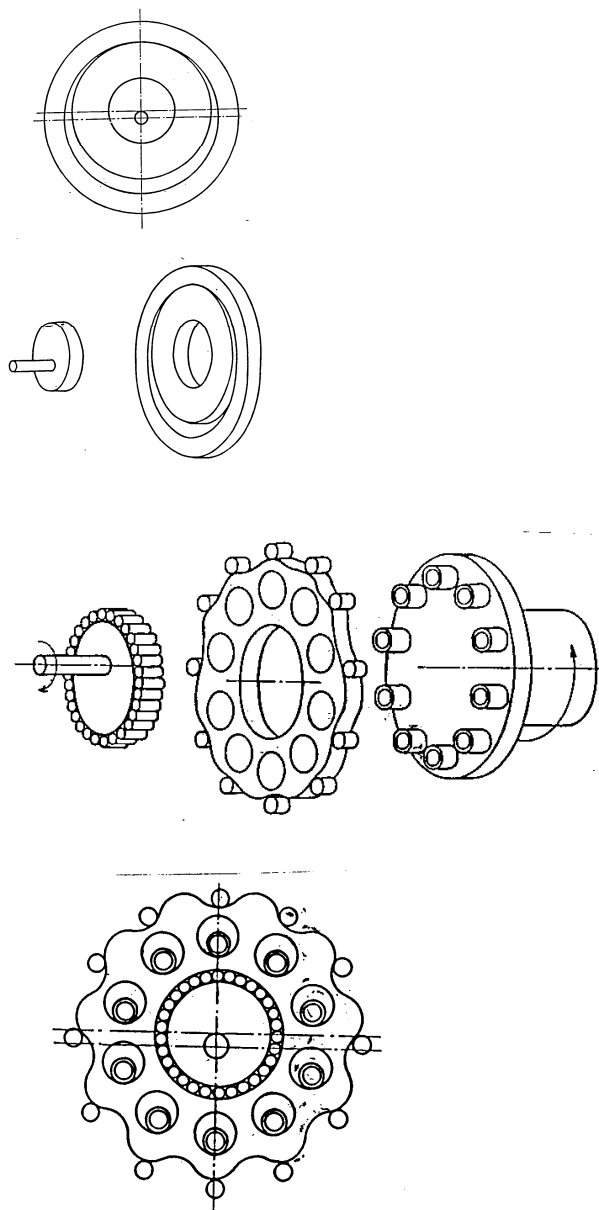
7 Úpravy k zabudování HP do kloubu robotu
